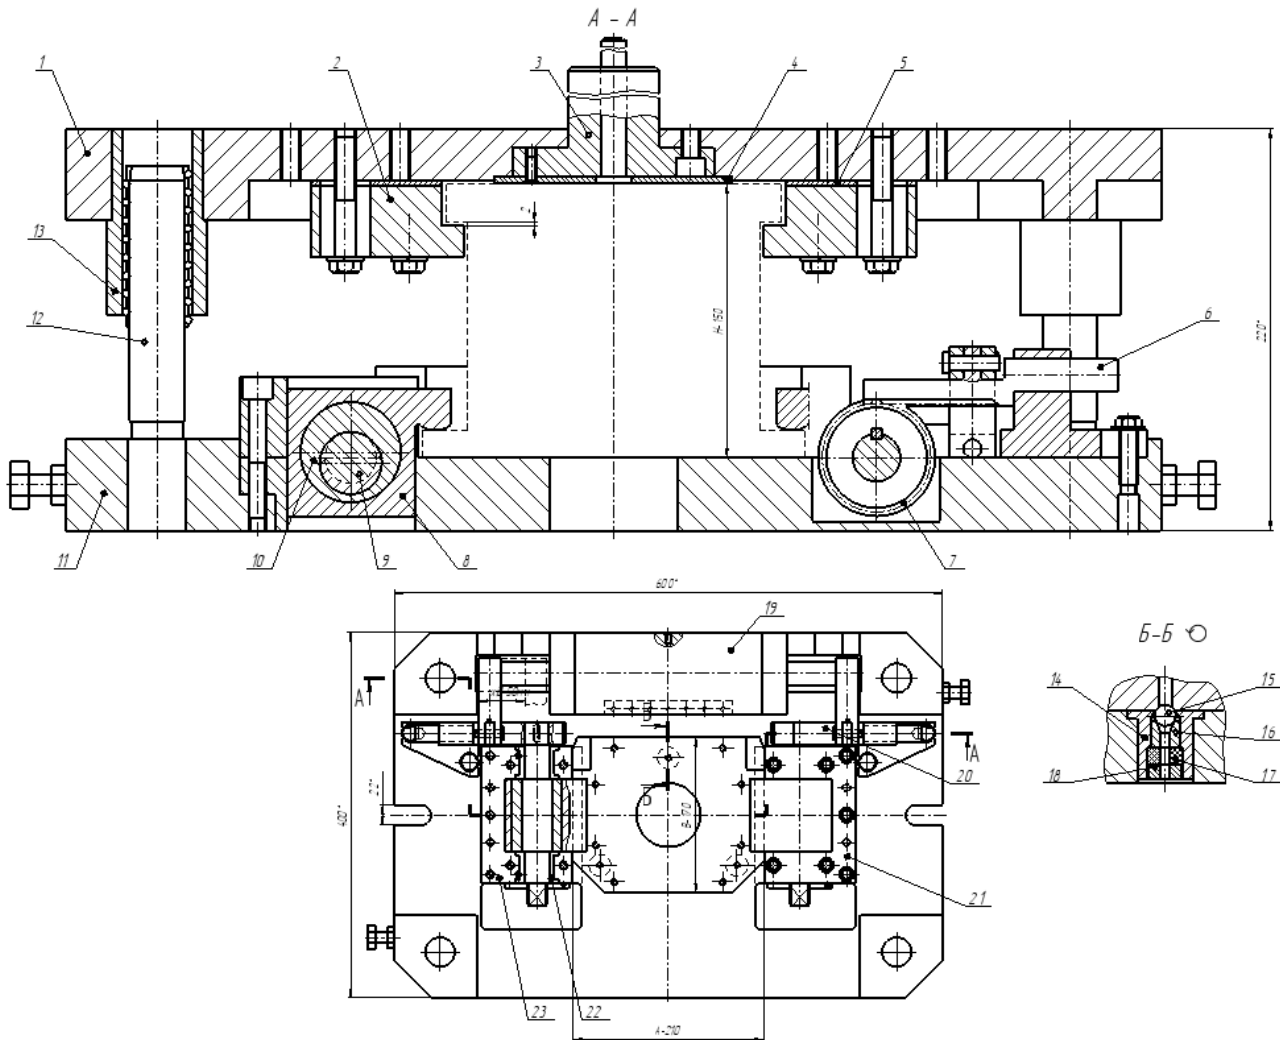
Ескіз блока швидкознімного кріплення: 1 – плита верхня; 2 – прихоплювач; 3 – хвостовик; 4 – пластина підкладна; 5 – підкладка; 6 – рейка зубчаста; 7 – шестерня; 8 – повзун затискний; 9 – вал ексцентриковий; 10 – шатун; 11 – плита нижня; 12 – напрямна колонка; 13 – напрямна втулка; 14 – втулка; 15 – кулька; 16 – гніздо; 17 – кільце гумове; 18 – пробка; 19 – пневмоциліндр; 20 – кронштейн; 21 – корпус; 22 – підшипник; 23 – кришка
